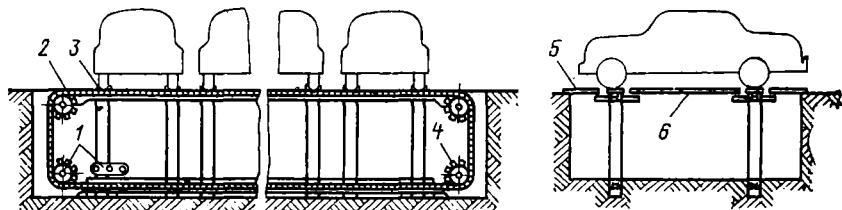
Схема несущего конвейера с поперечным перемещением автомобилей:
